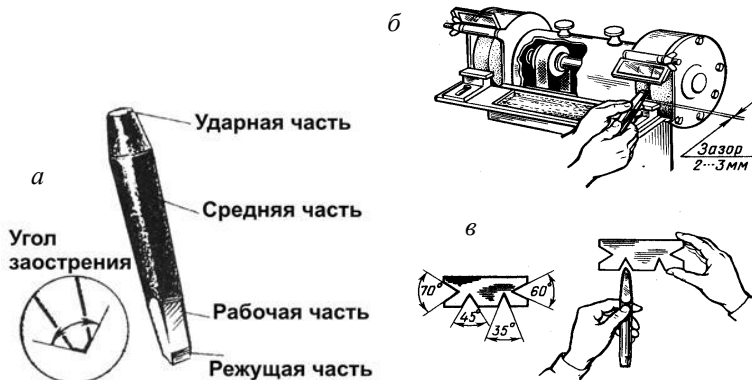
Конструкция зубила (а), приемы держания зубила при заточке зубила на заточном станке (б) и шаблон для проверки правильности угла заточки (в)
